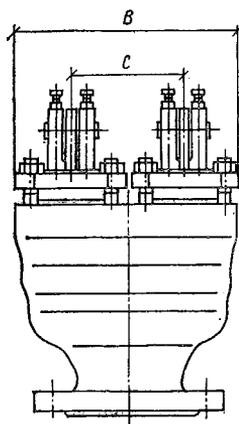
Клапан предохранительный малоподъемный однорычажный фланцевый 17кч3бр.
